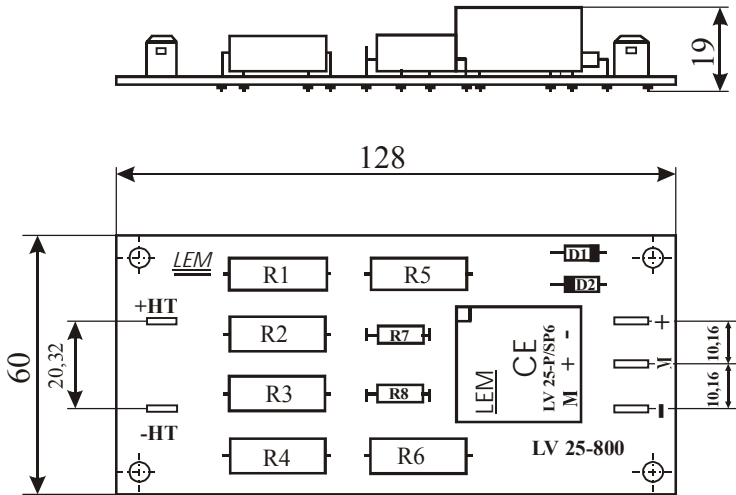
Внешний вид и габаритные размеры датчиков напряжения типа LV 25-800
